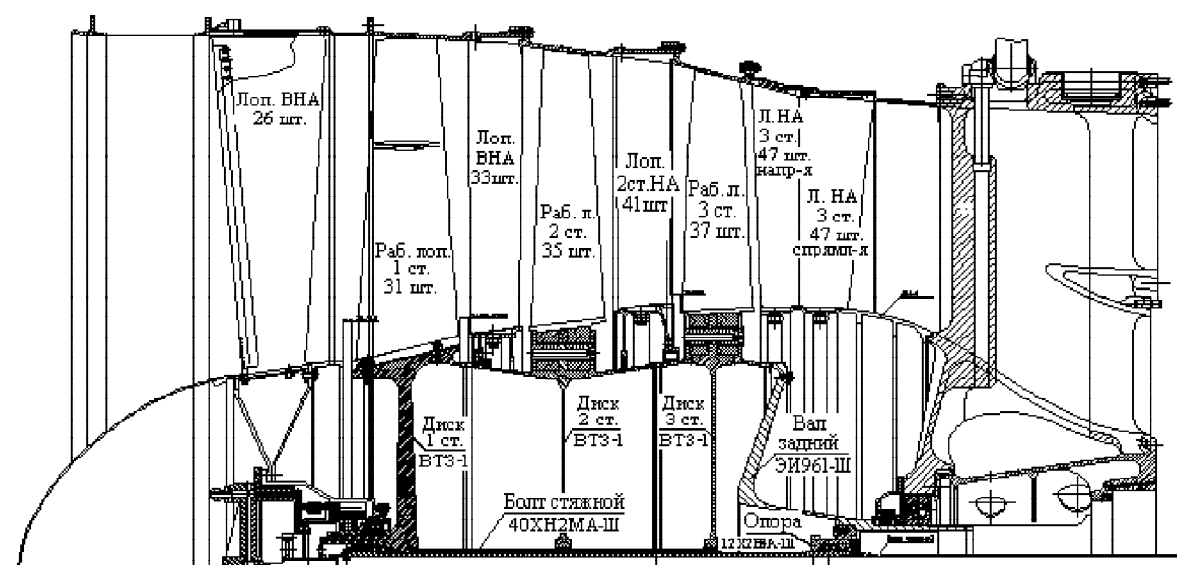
Схема ротора КНД двигателя семейства Д-30 в сборе
